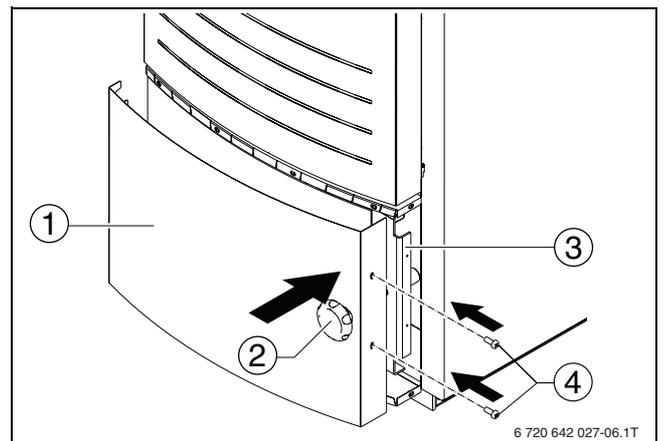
Montaggio del rivestimento della porta della camera di combustione
